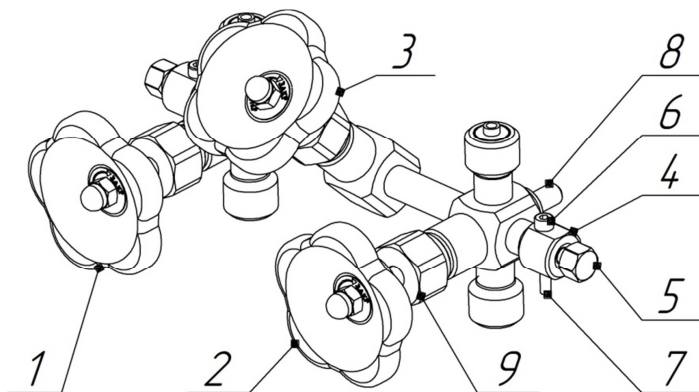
Конструктивная схема изделия: 1, 2 – запорные вентили; 3 – уравнительный вентиль; 4 – сбросной клапан; 5 – игла сбросного клапана; 6 – трубка сливная; 7 – винт стопорный; 8 – шпилька крепления; 9 – нажимная гайка
